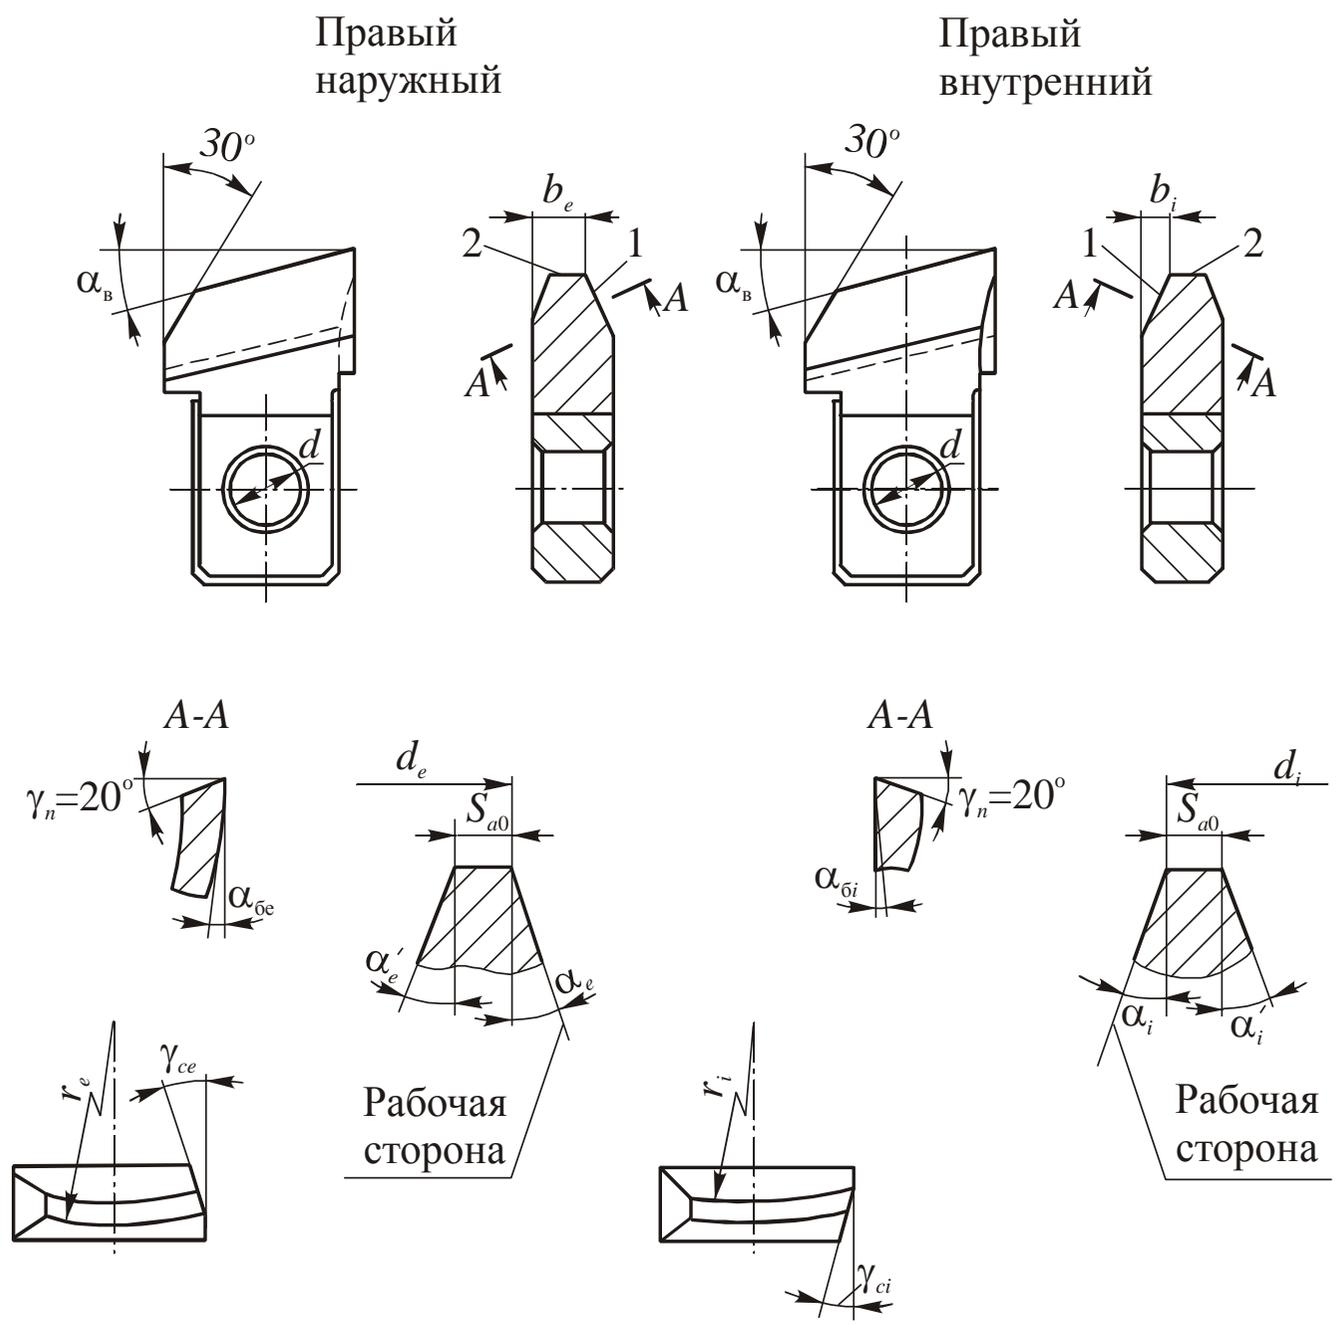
Чистовые резцы зуборезной праворежущей головки
